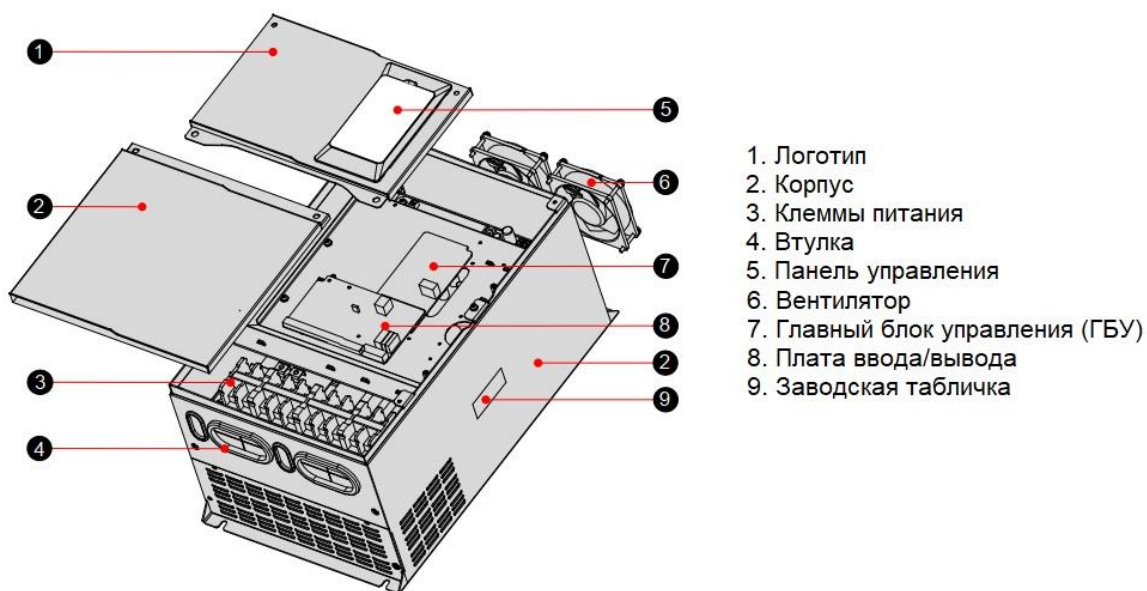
Покомпонентный вид INVERTER (18.5–45 кВт, корпус из листового металла)
